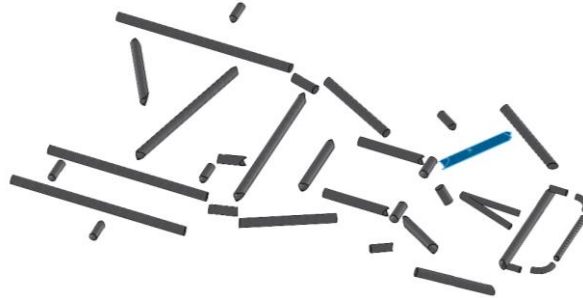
Miembros estructurales flotantes dentro del ensamblaje.
